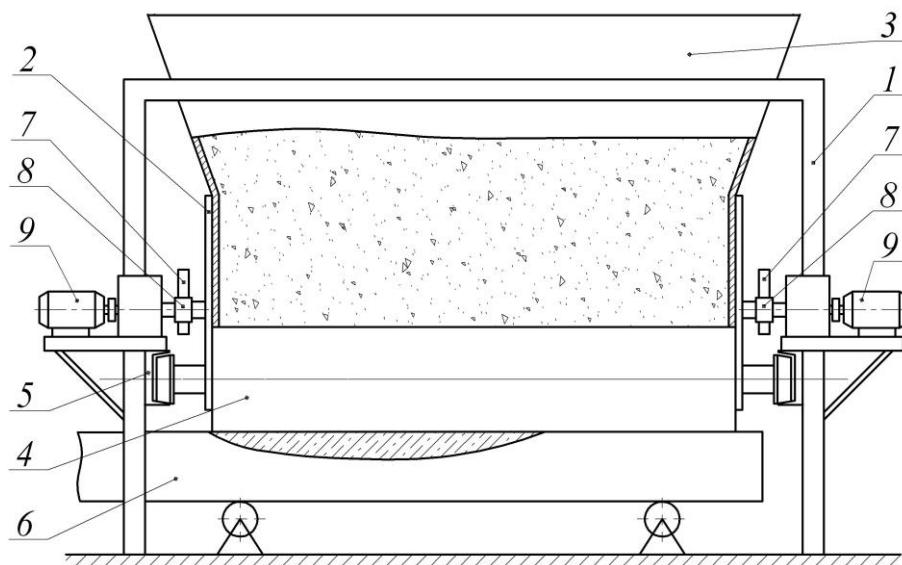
Роликова формувальна установка з кулачковим приводним механізмом
